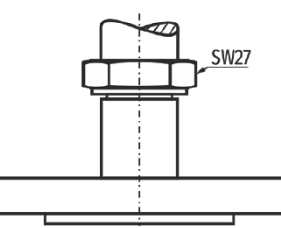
Исполнения корпусов. Внешний вид, габаритные размеры
